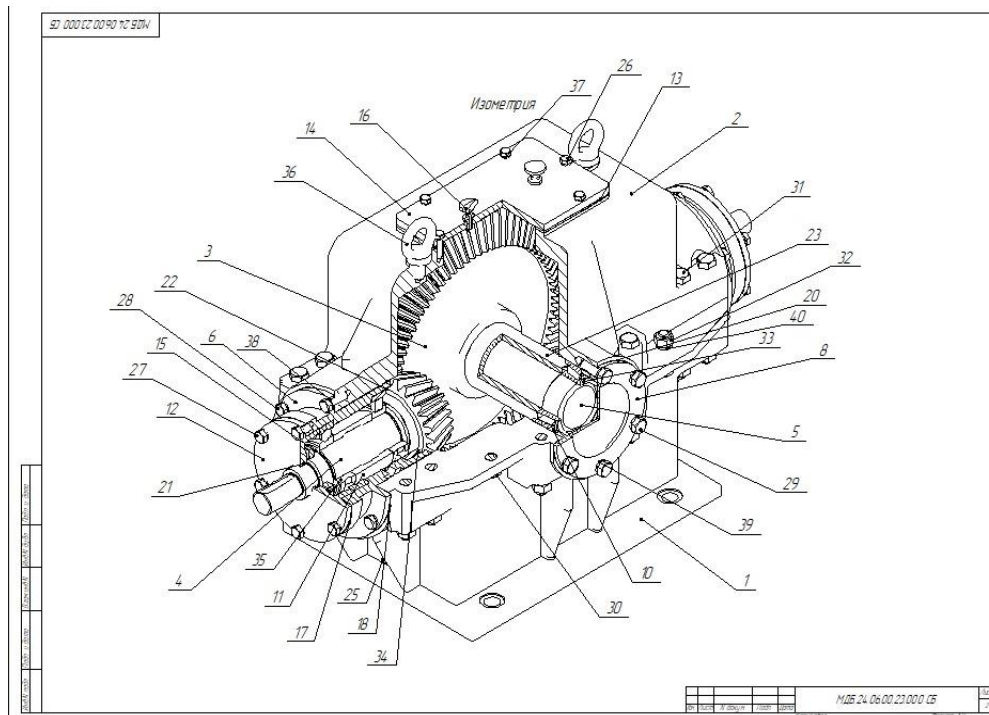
Сборочный чертеж мультипликатора (общий вид с разрезом)
